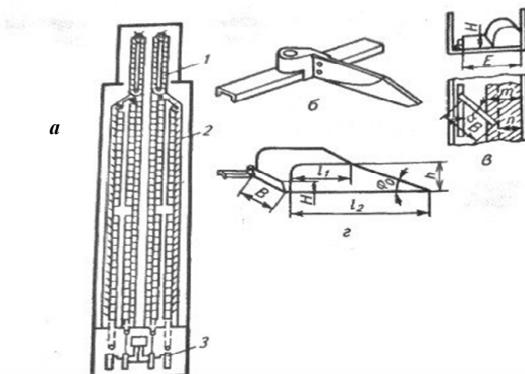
Скребковый навозоуборочный транспортер возвратно-поступательного движения (штанговый):
